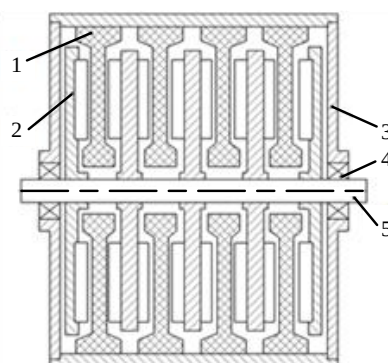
Модульная дисковая машина: 1 – обмотка статора; 2 – роторный узел; 3 – корпус; 4 – подшипники; 5 – вал
